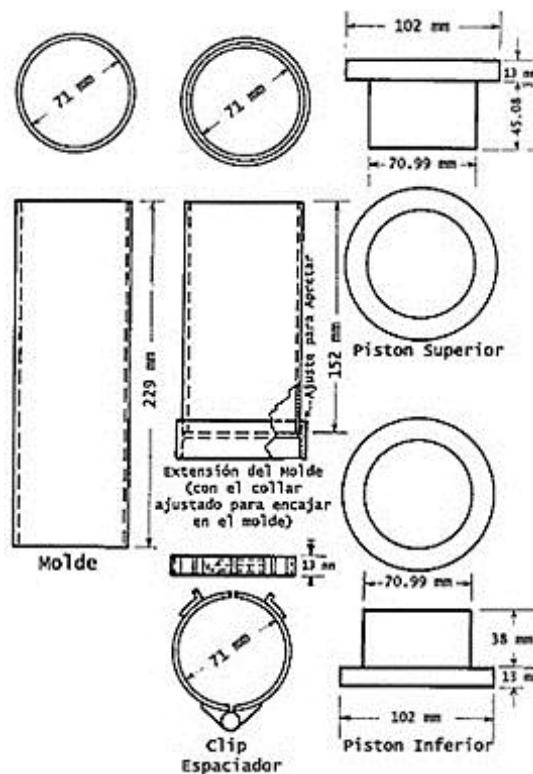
Moldes Cilíndricos para Suelo Cemento (dimensiones en mm)
